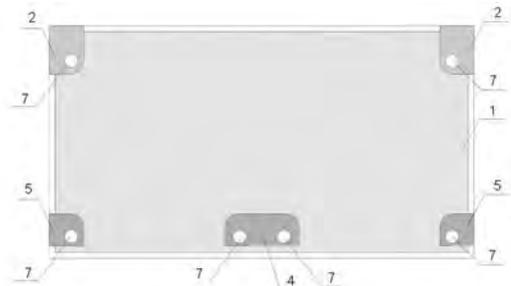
Модернизированный стол для укладки заготовок с базирующими элементами:
